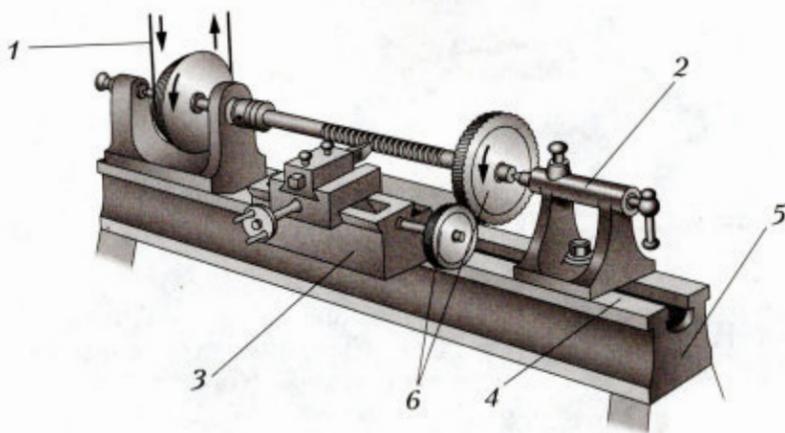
Токарно-винторезный станок Модсли с приводом от паровой машины, оснащённый механическим суппортом (-1800 г.): 1 – привод; 2 – задняя бабка; 3 – крестовой суппорт (имел два ходовых винта, причём поперечный приводился в движение вручную); 4 – направляющая; 5 – станина; 6 – сменные зубчатые колёса (позволяли изменять передаточное отношение между заготовкой и ходовым винтом)
